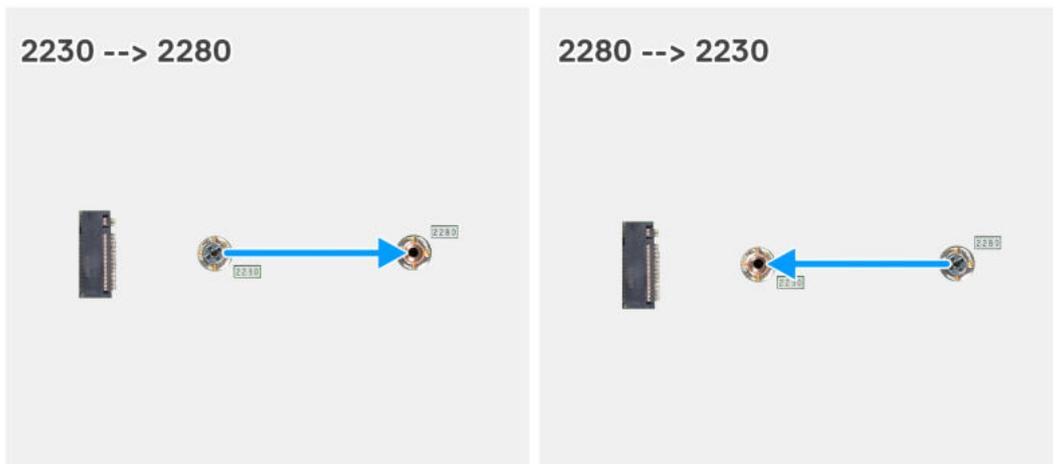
Verschieben der Solid-State-Schraubenhalterung auf M.2-Steckplatz 0
